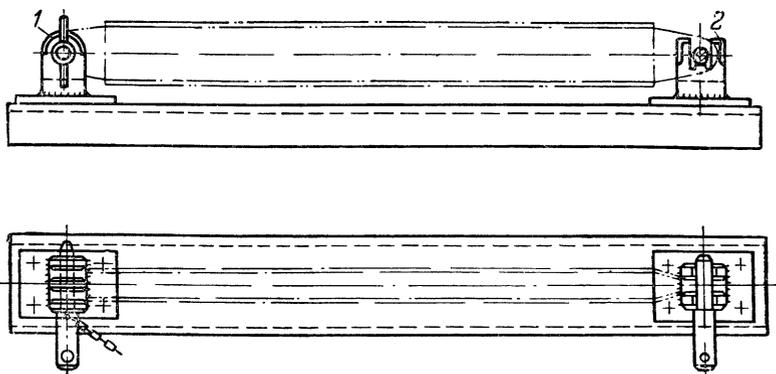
Шаблон для проверки расположения патрубков коллектора.
